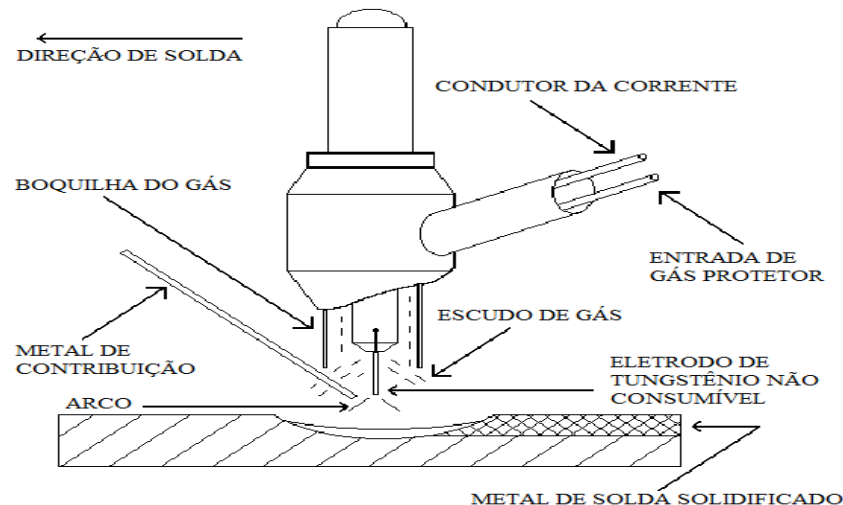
Esquema de solda com eletrodo de tungstênio e gás (GTAW). Fonte: Manual de Solda, (1999).
